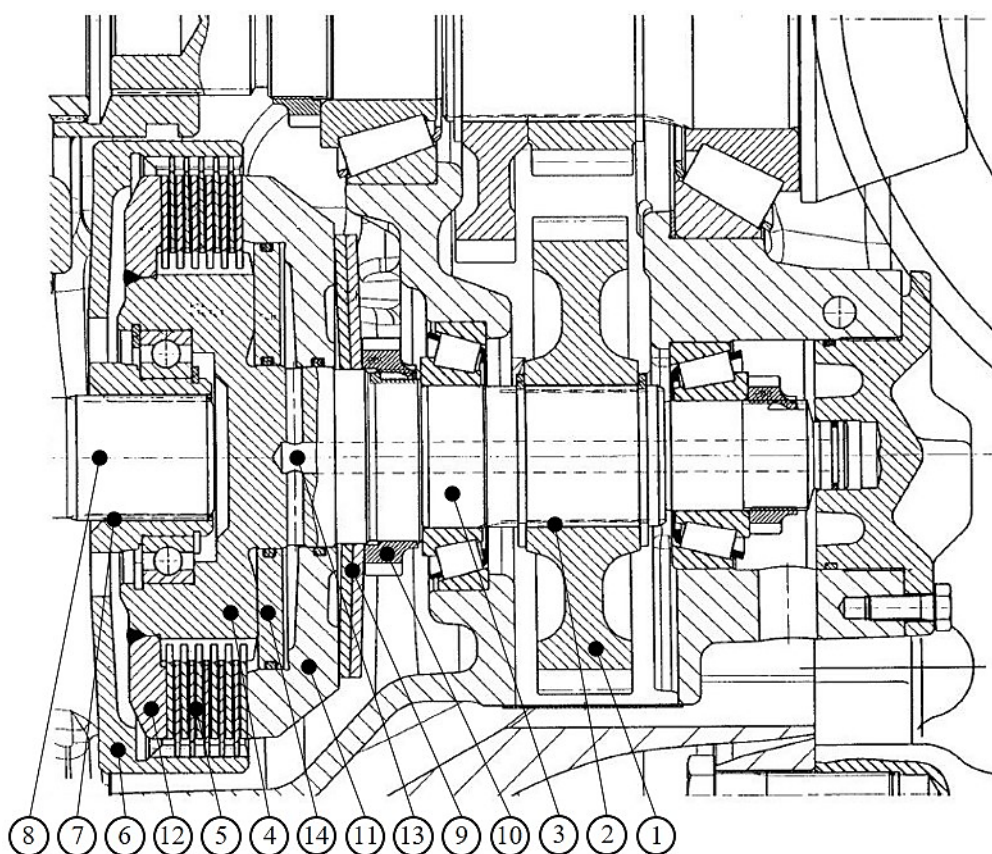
Primárně rozpojená spojka pohonu přední nápravy traktoru [5][3]
